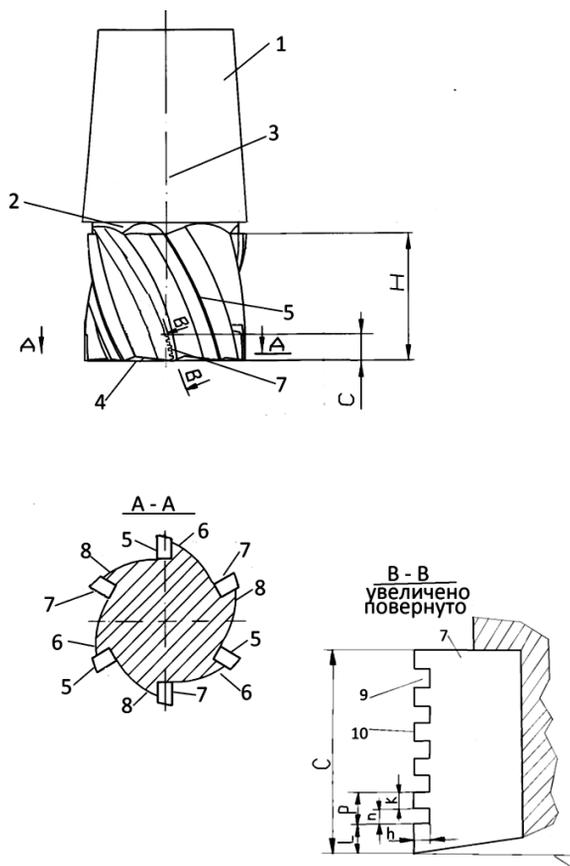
Концевая фреза с комбинированными режущими зубьями в торцевой части
